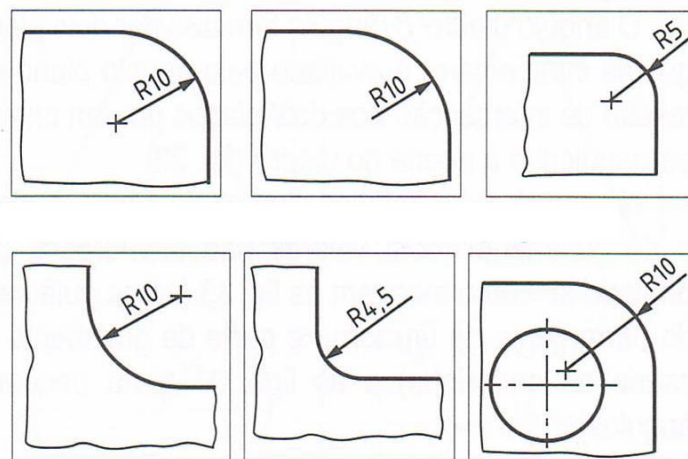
Representação em desenho técnico de cotagem de raios.
